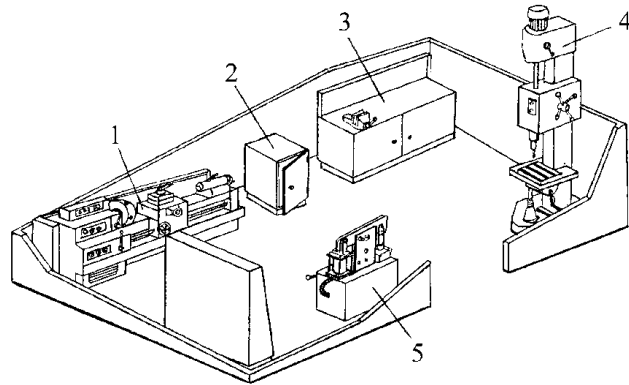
Слюсарно-механічна дільниця: 1 – універсальний токарно-гвинторізний верстат 1В62Г; 2 – тумбочка інструментальна ОРГ-1611; 3 – верстак слюсарний з настільним точильно-шліфувальних верстатом ЗЕ631; 4 – верстат радіально-свердлильний 2К52-1; 5 – універсальна установка для ремонтних робіт ОР-12561.
